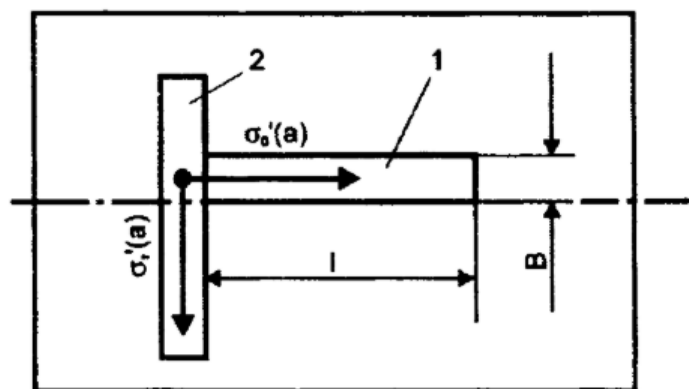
Схема вырезки образцов для определения остаточных напряжений в деталях типа пластин и цилиндров: 1 – продольный образец; 2 – поперечный (или кольцевой)
